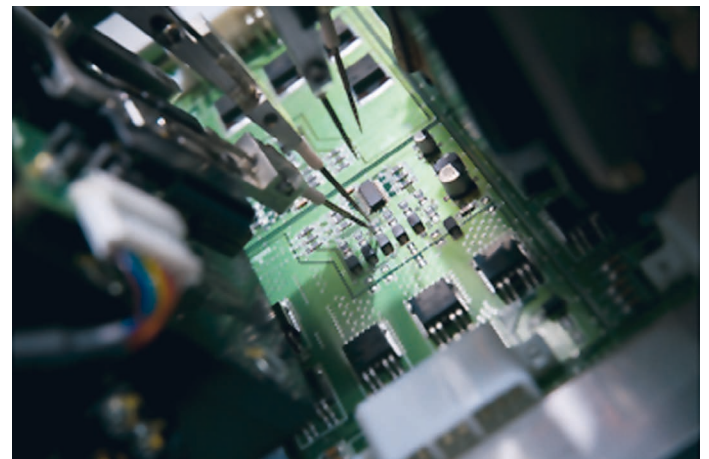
Es ist wichtig, beim Design das Prüfen zu berücksichtigen und ausreichend Testpunkte im PCB Layout bereitzustellen. Die richtige PCB Layout Software kann beim schnellen und einfachen Design für Test helfen
